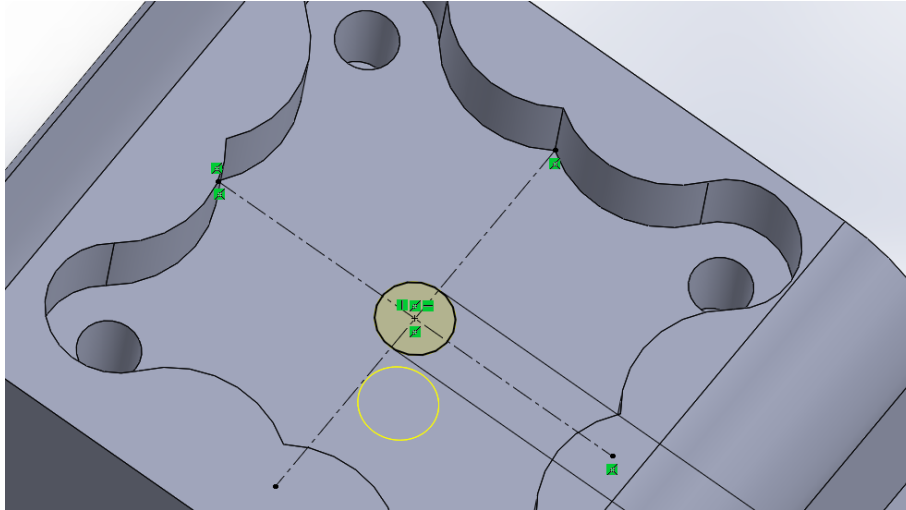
Cut-Extrude do furo central do dispositivo de fixação.
